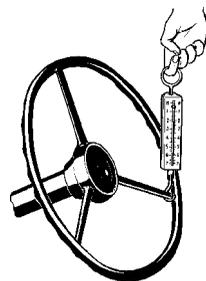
Проверка затяжки подшипников червяка при помощи динамометра
